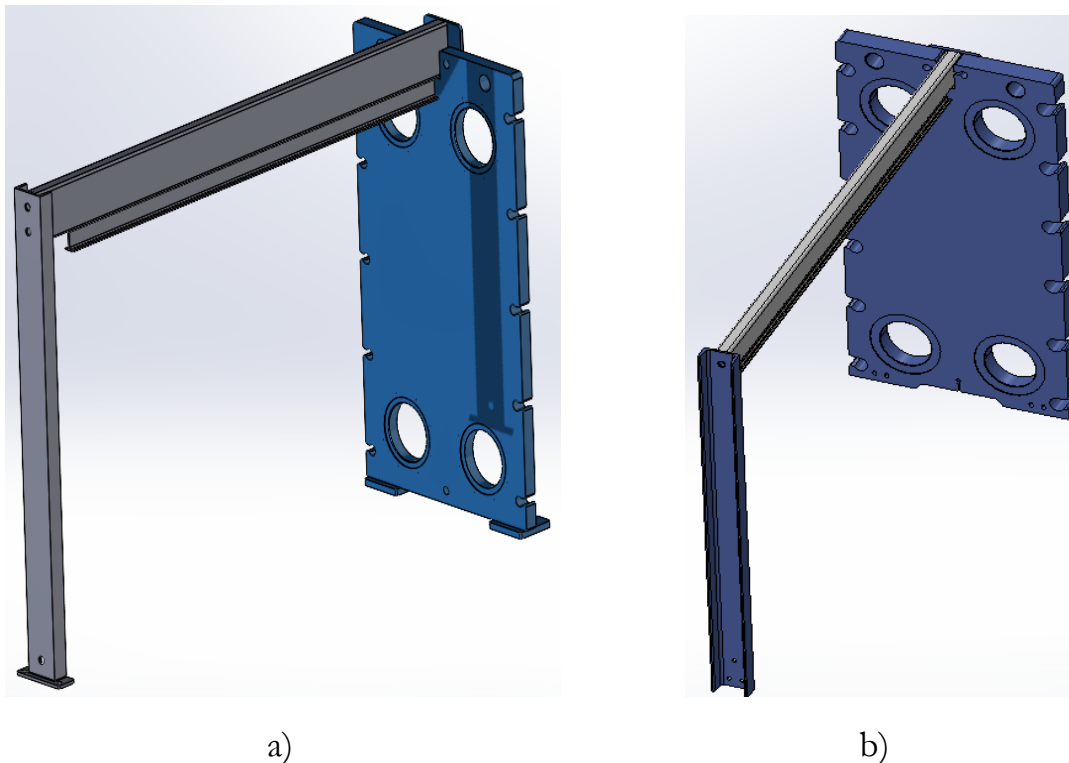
Tirante superior: a) desenhado; b) WH30.
